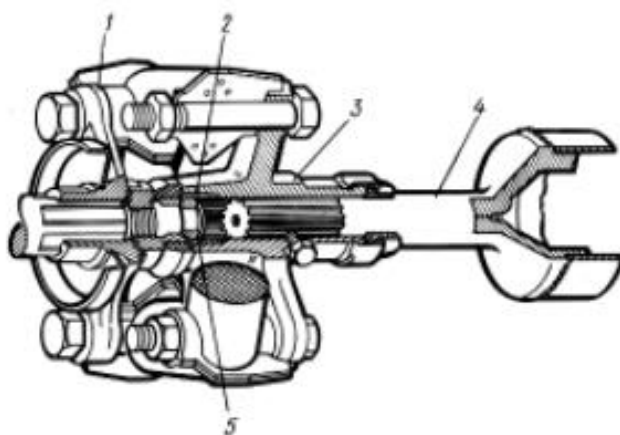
Карданная передача с упругим полукарданным шарниром: 1 – фланец вторичного вала КПП; 2 – гайка крепления фланца 1; 3 – фланец карданного вала; 4 – карданный вал; 5 – центрирующее кольцо;
